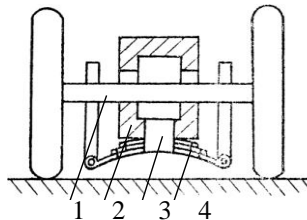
Підресорювання пластинчастою ресорою:
